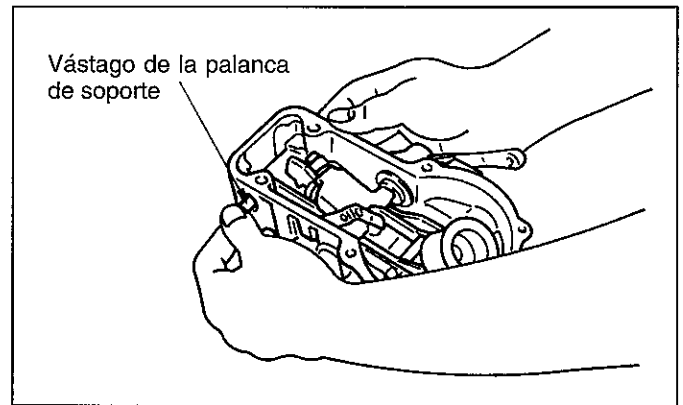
Desmontaje del vástago de la palanca de soporte
